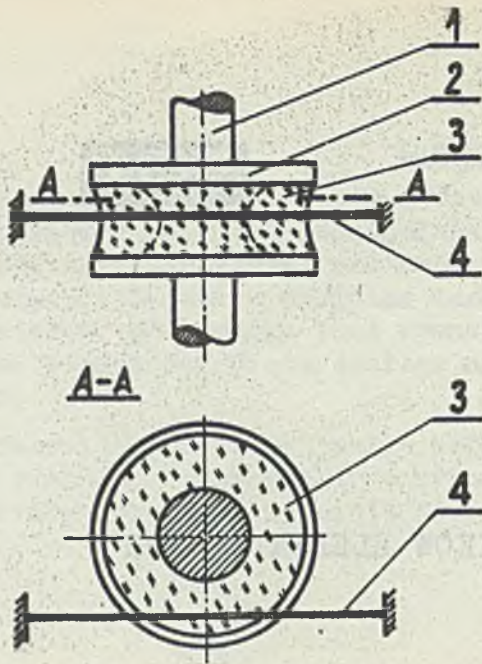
Łożysko sztywne wypełnione cieczą: 1 - oś, 2 - oprawa, 3 - ciecz, 4 - kamień łożyskowy
